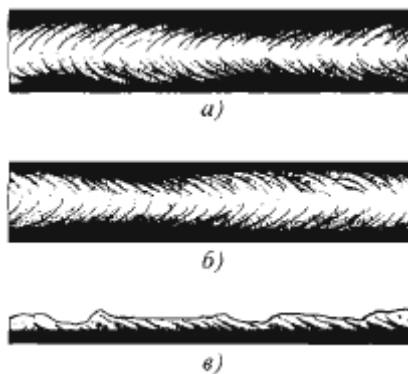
Дефекты формы швов: неравномерная ширина шва при ручной сварке, неравномерная ширина шва при автоматической сварке, неравномерная выпуклость шва – бугры, впадины.
